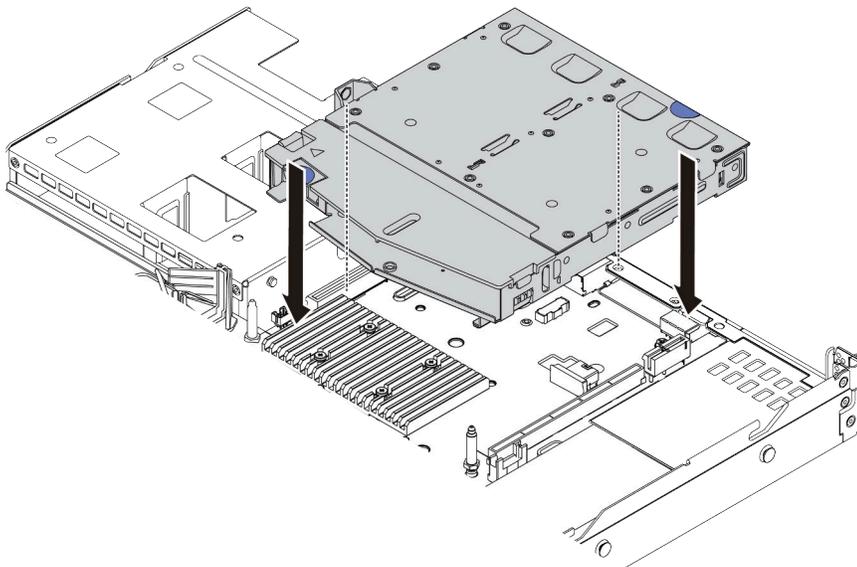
Installation der hinteren Hot-Swap-Laufwerkshalterung
